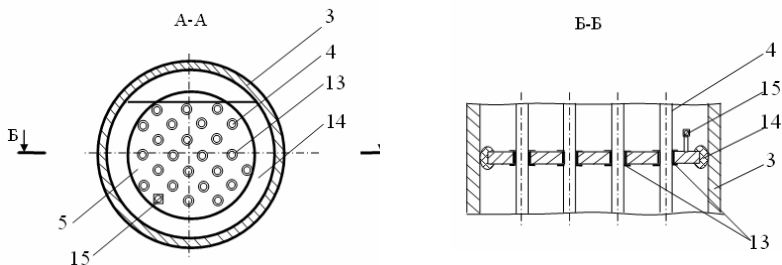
Поперечный разрез по А-А и поперечный разрез перегородки по Б-Б
